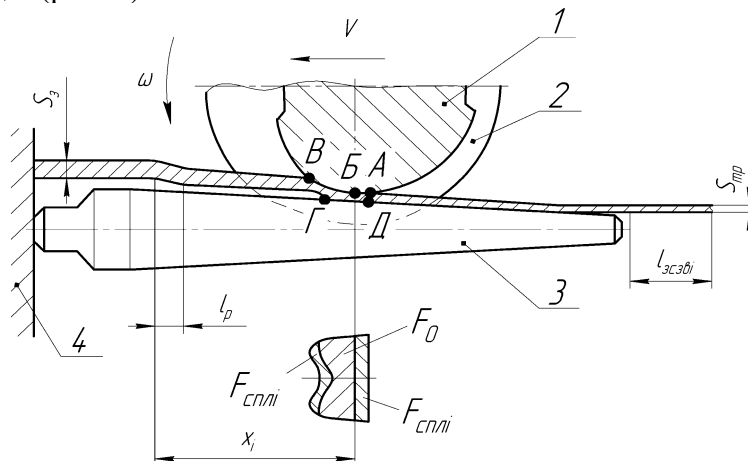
Схема сумарного та миттєвого осередку деформації при деформуванні труби - заготовки зворотним ходом кліті: 1- валок; 2 - рівчак валка; 3 - нерухома оправка; $Sз$ – товщина стінки труби-заготовки; $Sпр$ – товщина стінки прокатої труби; АБВГД- миттєвий осередок деформації; V - поступова швидкість валка; ω - кутова швидкість валка; $lзсзвi$ - лінійний зсув переднього торця труби; $lр$ - довжина зони редукування; Fo - горизонтальна проекція площі контакту рівчака валка з трубою, що деформується; $Fсплi$ – площа збільшеної частини площі контакту рівчака з трубою за рахунок сплюснення валка; Xi – довжина від початку деформованої труби-заготовки до положення валка і
